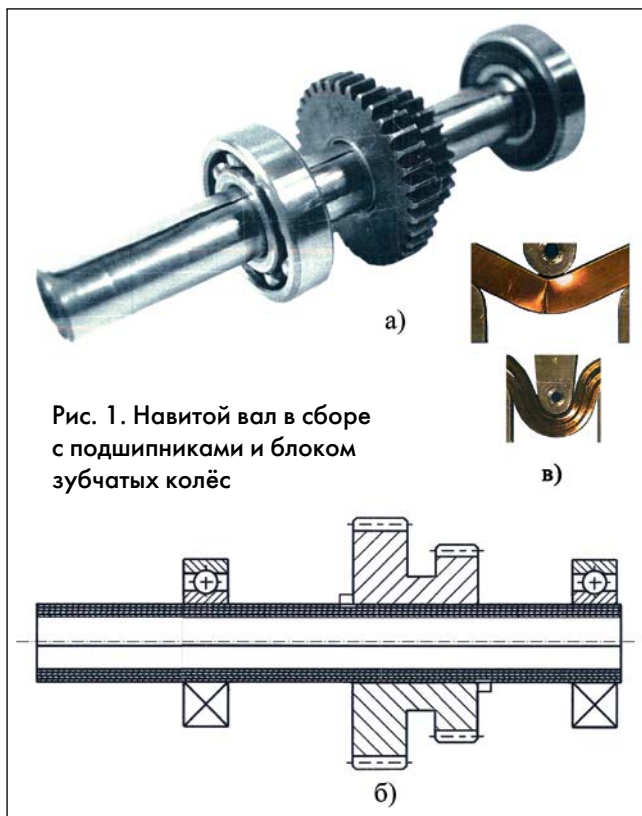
Навитой вал в сборе с подшипниками и блоком зубчатых колёс
